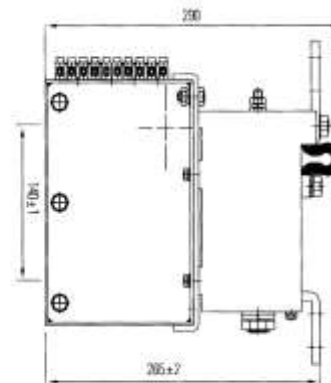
Габаритные размеры КВТ-1,14-1000/1250
